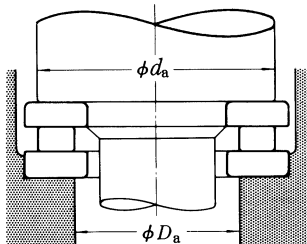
Диаметры поверхности опор для упорных роликоподшипников
